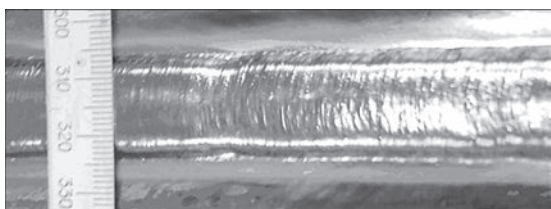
Характер формирования поверхности металла, наплавленного порошковой проволокой ППТ-22 на пластину сплава ВТ22
